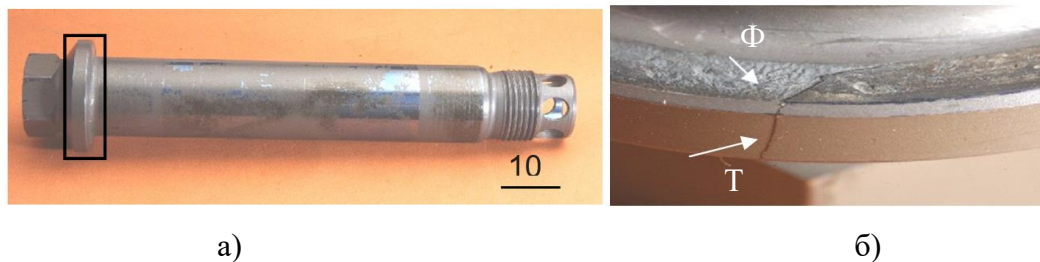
Разрушение болта вилки лопасти несущего винта вертолета [8].
